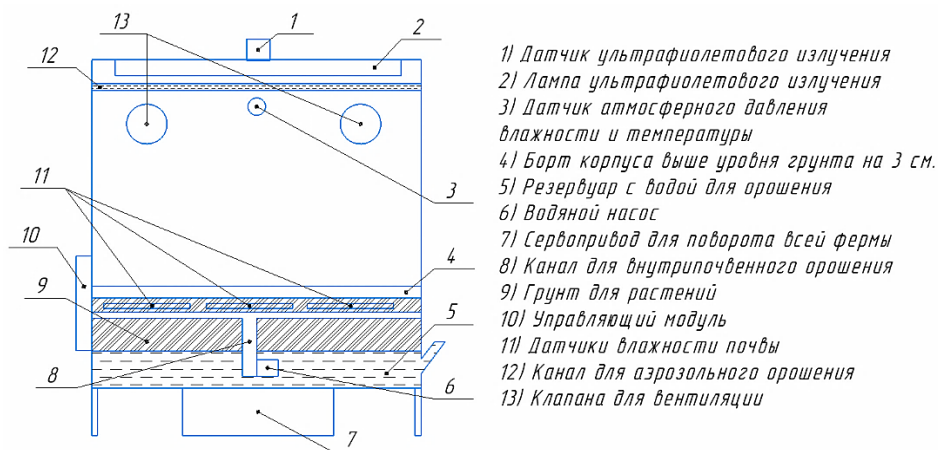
Конструкция корпуса фермы с расположением модулей
